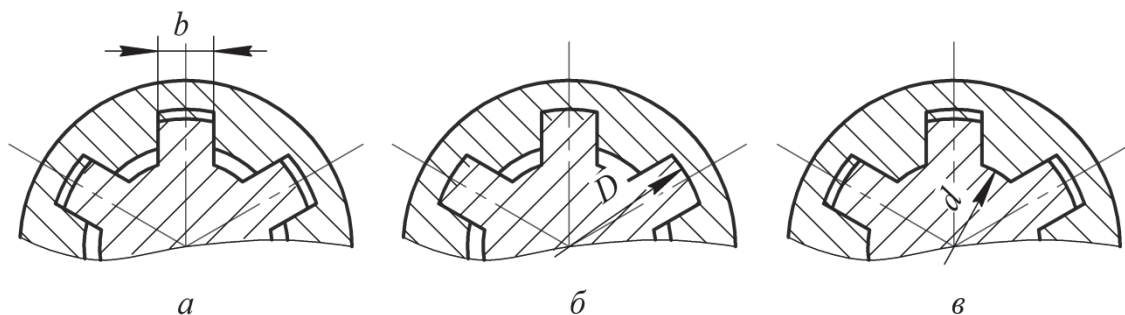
Размеры поперечного сечения и способы центрирования прямобочного шлицевого соединения
